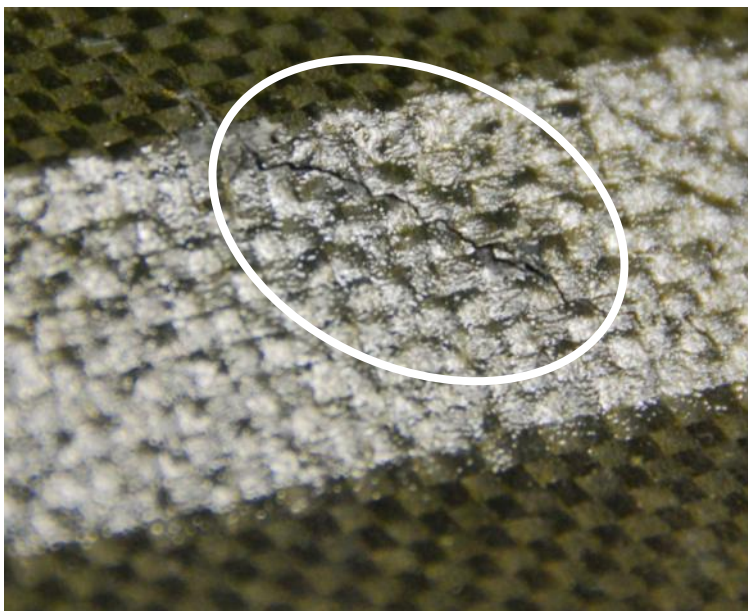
Photo d'une fissure sur le chanfrein d'un panneau après rupture.
